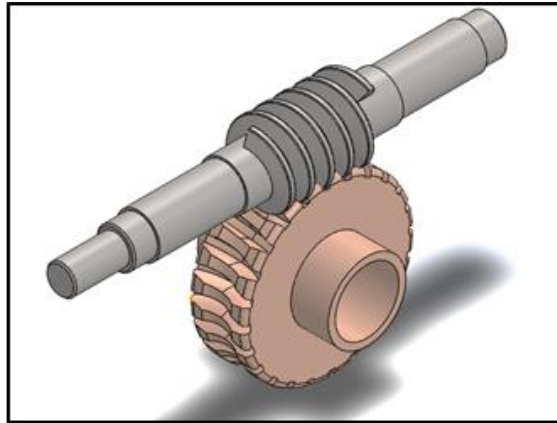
Vista isométrica, dimensiones y diseño de tornillo sinfín y corona.
